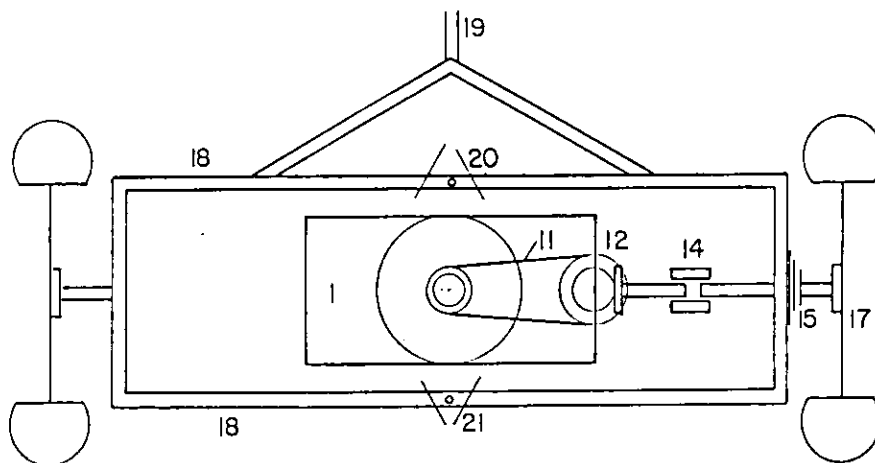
Esquema de montagem de plantadeira de alho para tração animal, em planta.
